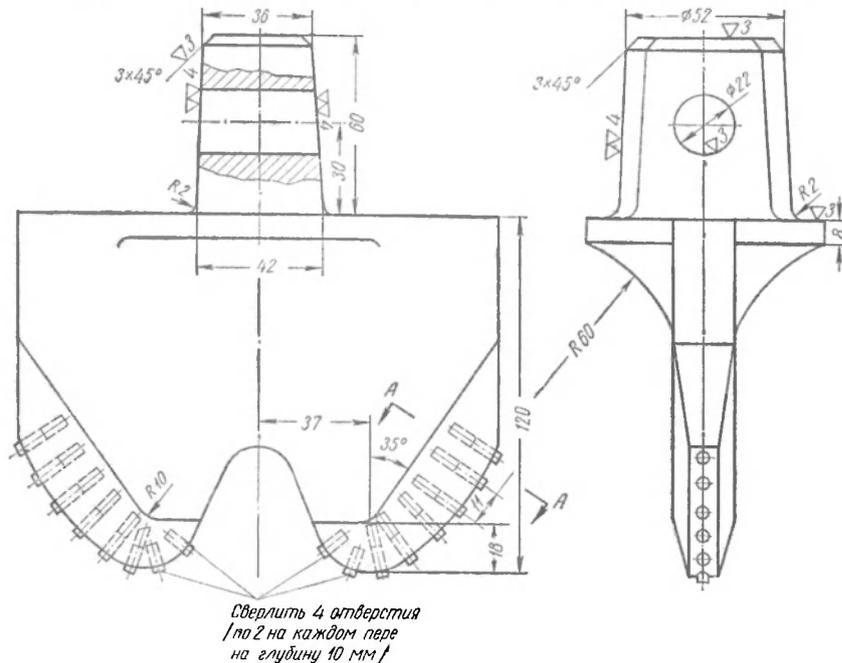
Резец 160 мм с профилем по кривой, обеспечивающей равномерный износ
